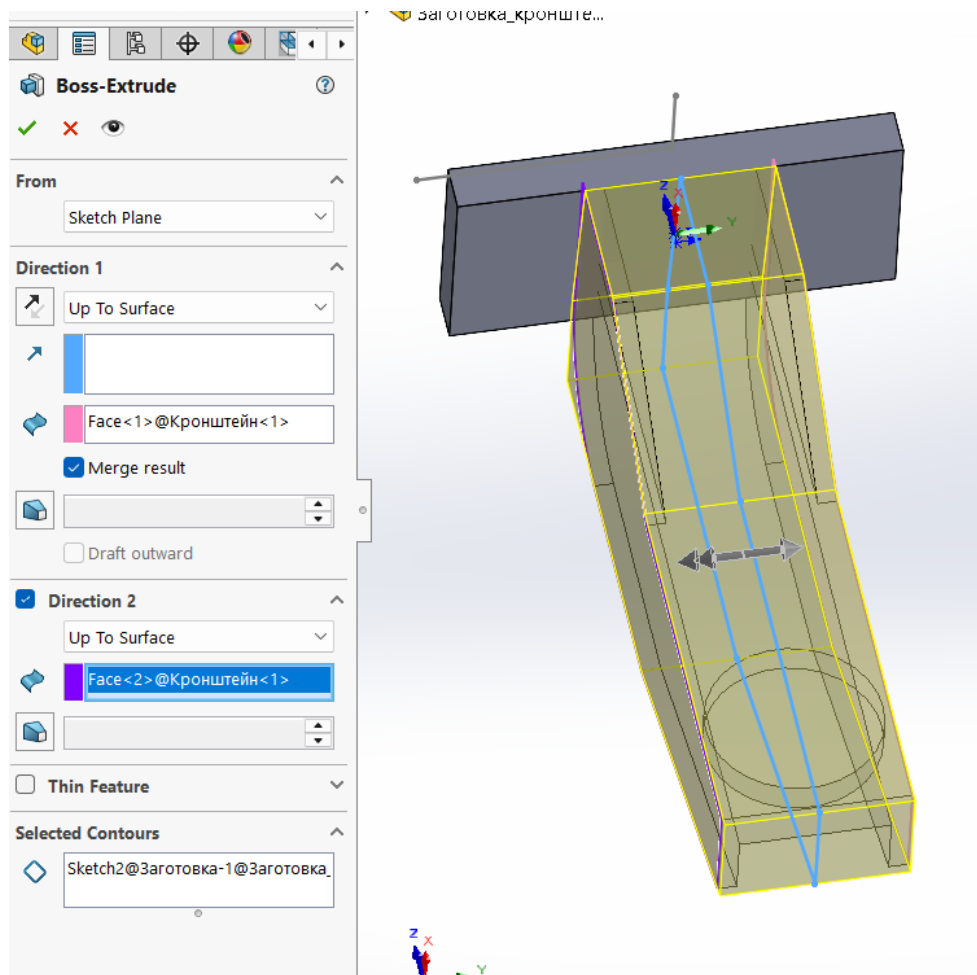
SolidWorks CAM з активною операцією Boss-Extrude для формування тіла заготовки з двостороннім витискуванням до поверхонь кронштейна
